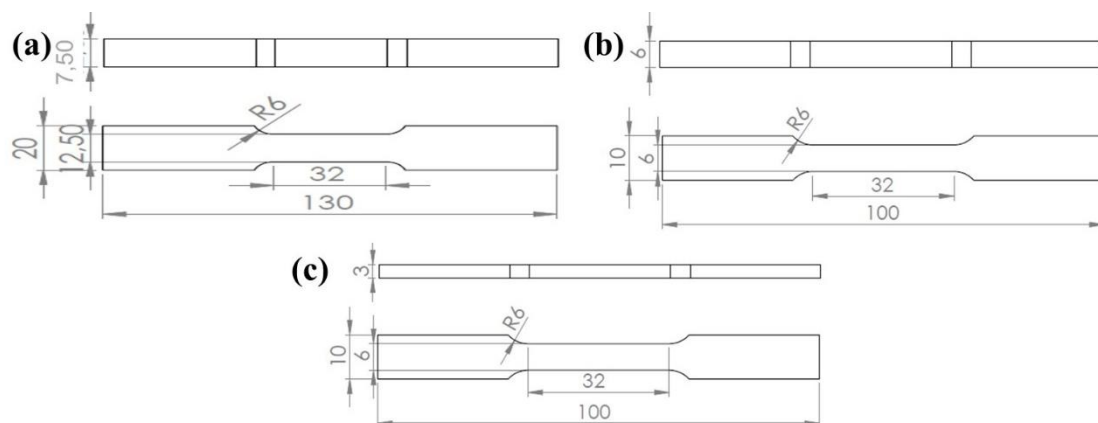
Dimensões dos corpos de provas, unidade em mm, utilizados para o ensaio de tração a temperatura ambiente. (a) condição CR, (b) condições Z5C e (c) condições C, C2, C3, Z5cA, Z5cA2, Z5cA3, Z5cR, Z5cR2 e Z5cR3.
